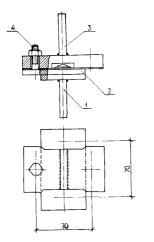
Общий вид приспособления 1-нижний захват: 2-кресто-
